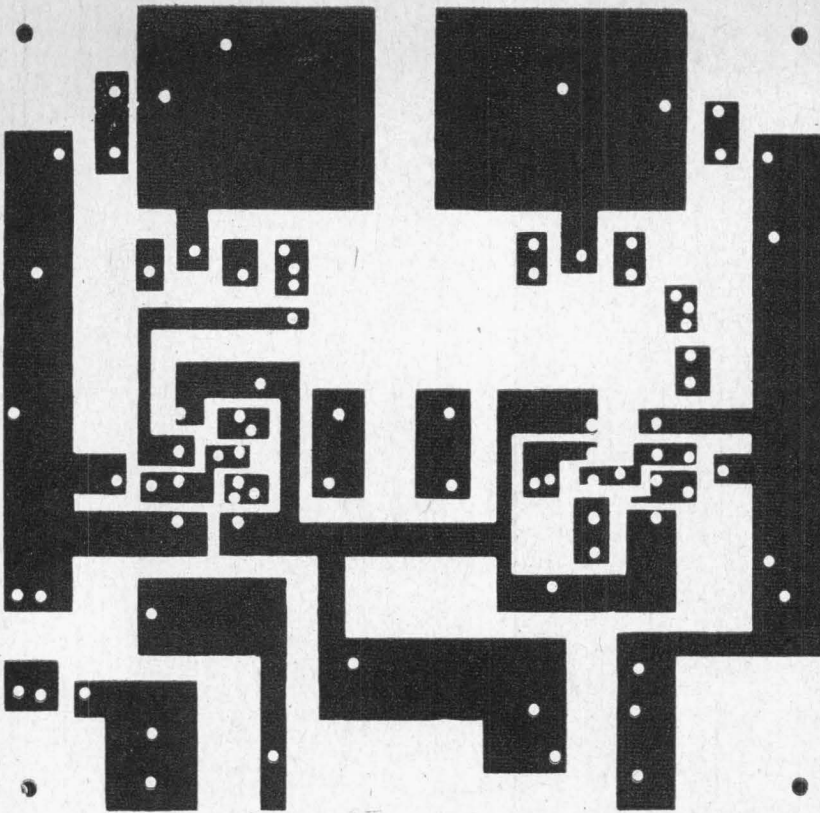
Plaqueta de circuito impresso para a montagem do pisca-pisca que mede 10 cm X 11 cm.
